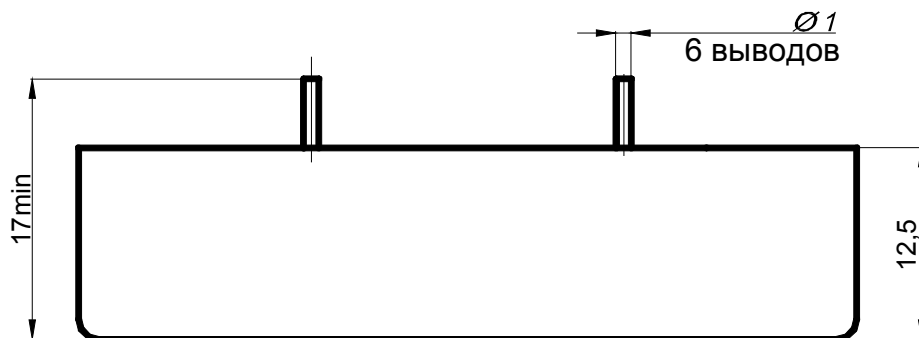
Габаритный чертеж модулей СМБ(Р)15
